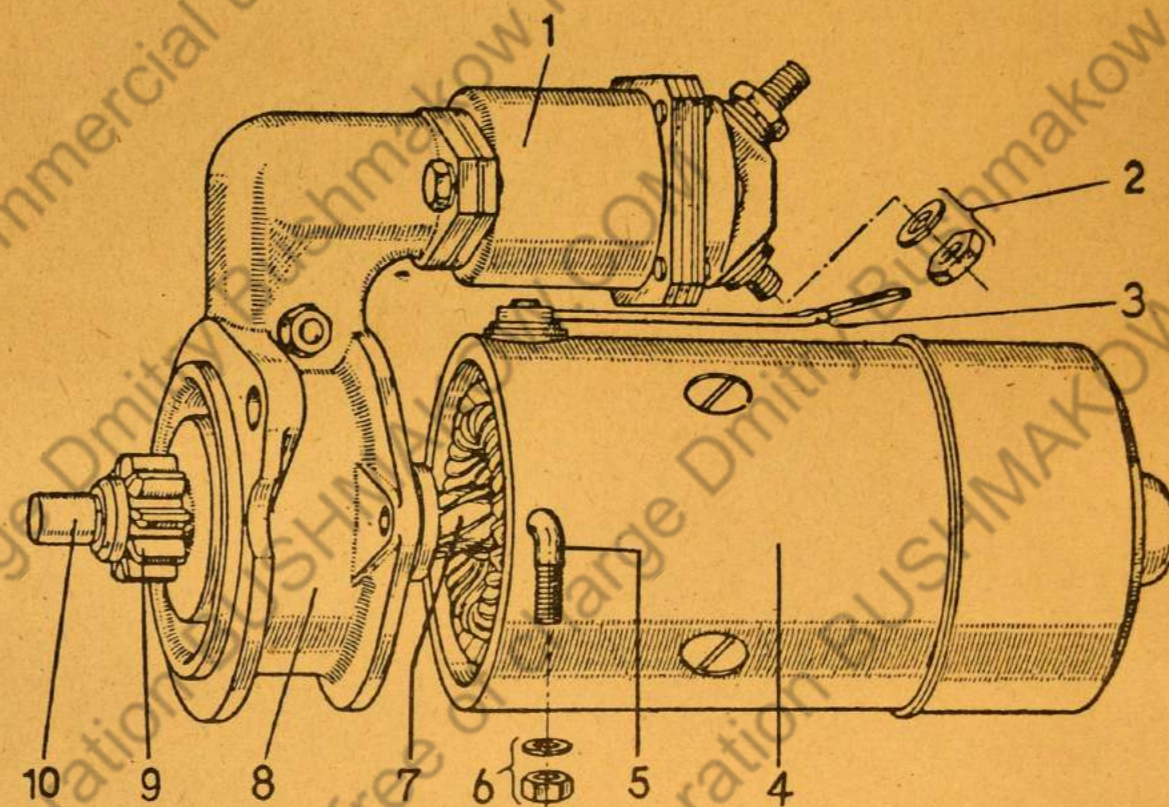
EED-Anlasser, Lagerhals nach dem Ritzel zu herausgezogen
